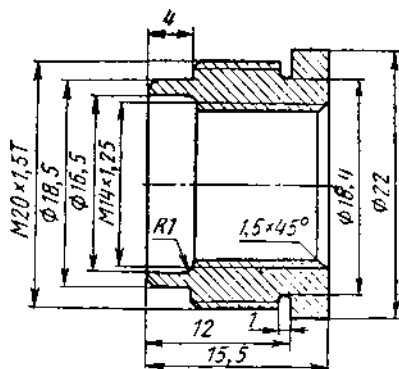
Чертеж втулки ремонтной под свечное отверстие
